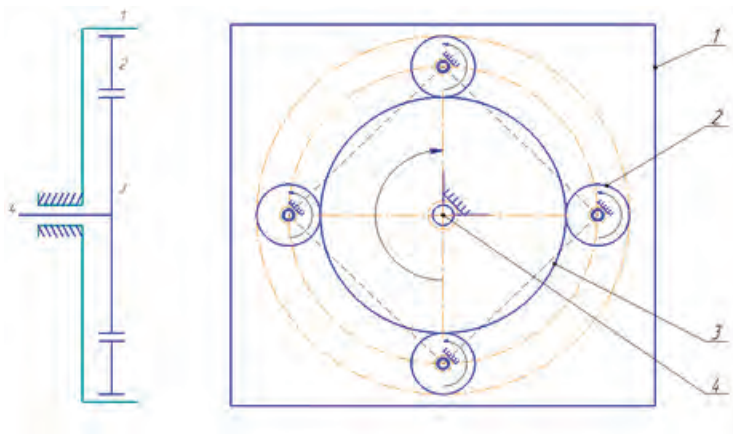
Общий вид прямозубой цилиндрической передачи
